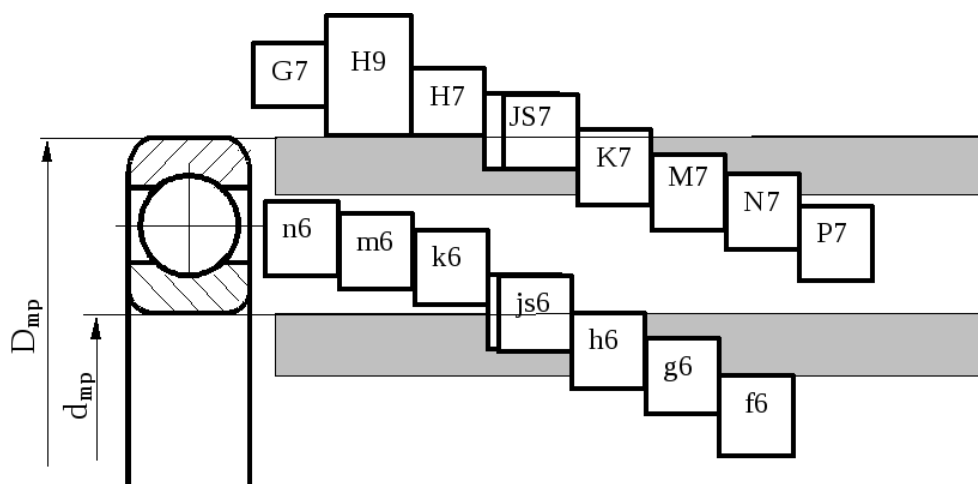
Схема расположения полей допусков для подшипников 0 и 6 классов точности
